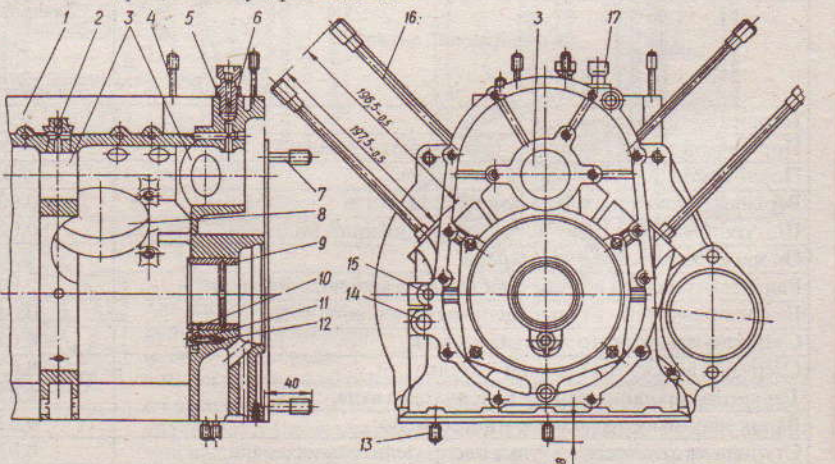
Ремонтные шпильки картера коленчатого вала: 1 - шпилька крепления головки цилиндров; 2 - шпилька крепления картера сцепления; 3 - шпилька крепления масляного радиатора; 4 - шпилька выпускной трубы
